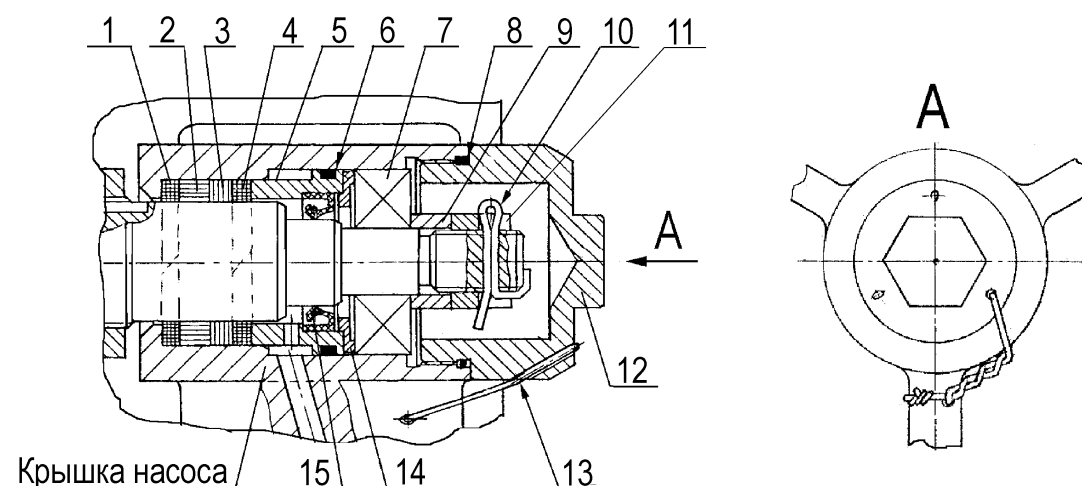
Уплотнение вала переднее: 1, 4 – кольцо уплотнительное из набивки; 2 – кольцо уплотнительное витое; 3 – кольцо уплотнительное слоеное; 5 – стакан; 7 – подшипник; 9 – втулка; 10 – шплинт; 11 – гайка; 12 – колпачок; 13 – проволока нержавеющей; 14 – кольцо, 15 – манжета; 6, 8 – кольца уплотнительные.
